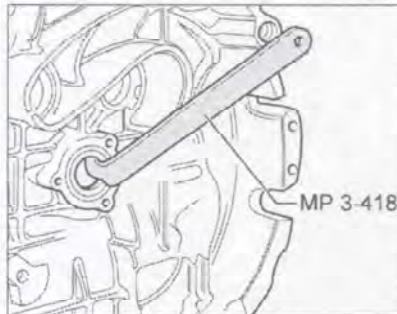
С помощью рычага MP 3-418 извлеките изношенный сальник первичного вала.
